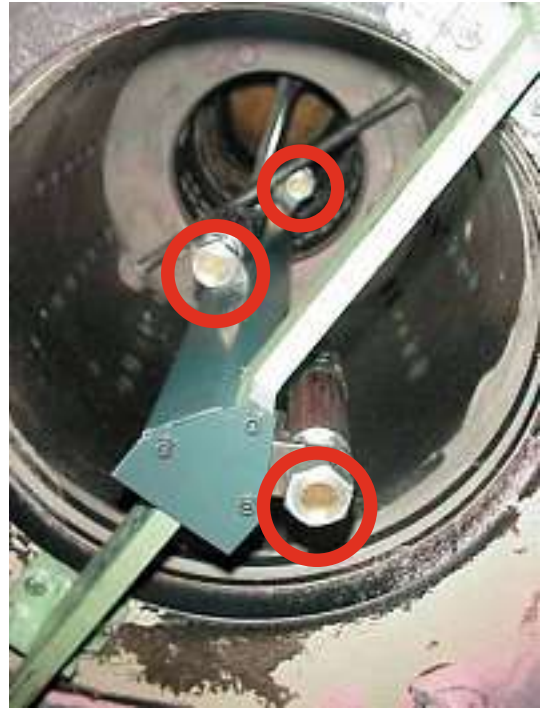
Drucksensoren 4, 6, 7 im Sandzylinder
